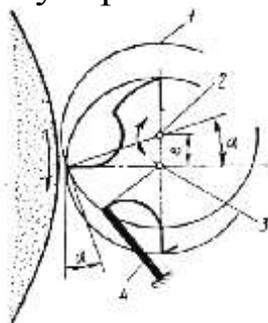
Схема затылования: 1 – цилиндр затылования; 2 – ось качания в центрах станка; 3 – ось метчика; 4 – упорка.
